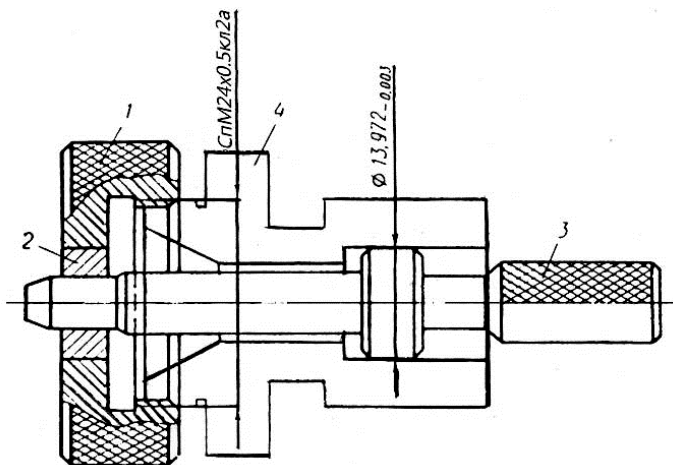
Калибр положения для контроля биения поверхностей оправы
